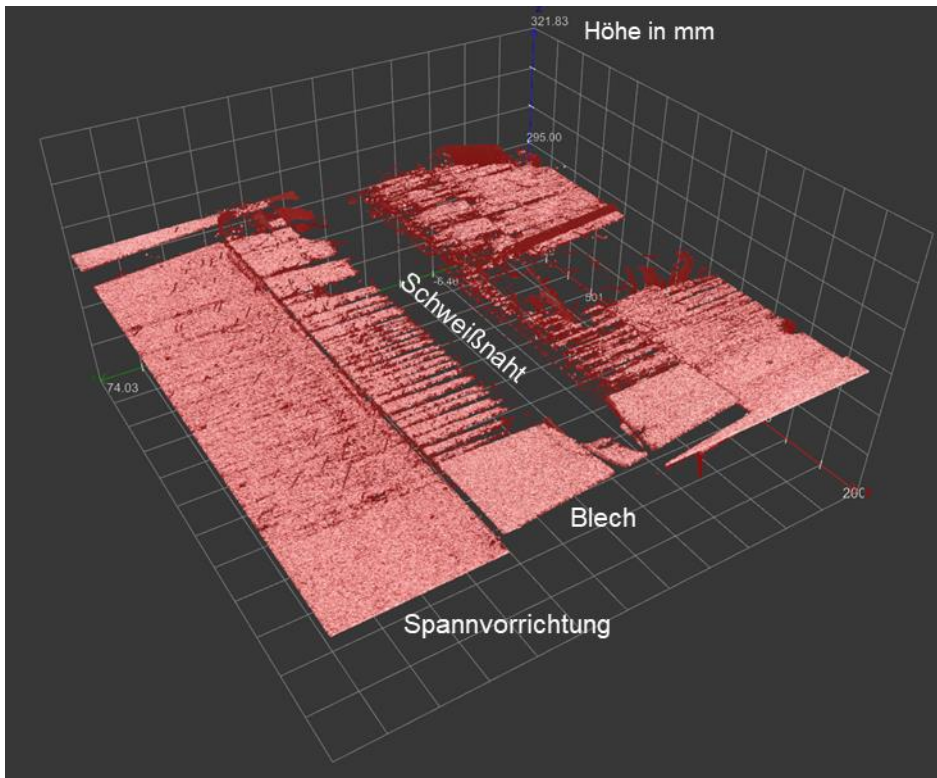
Auslöschung der Schweißnaht bei Messort auf der glühenden Schweißnaht
